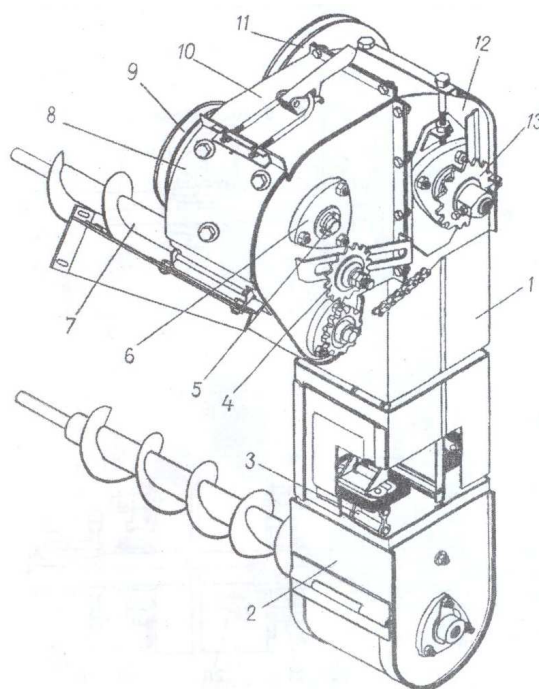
Колосовой элеватор и домлачивающее устройство
